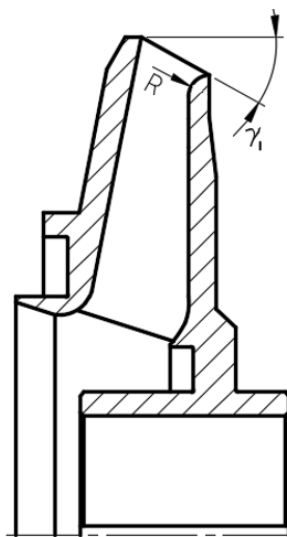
Схема скругления внутренней кромки ведущего диска рабочего колеса в первой схеме
